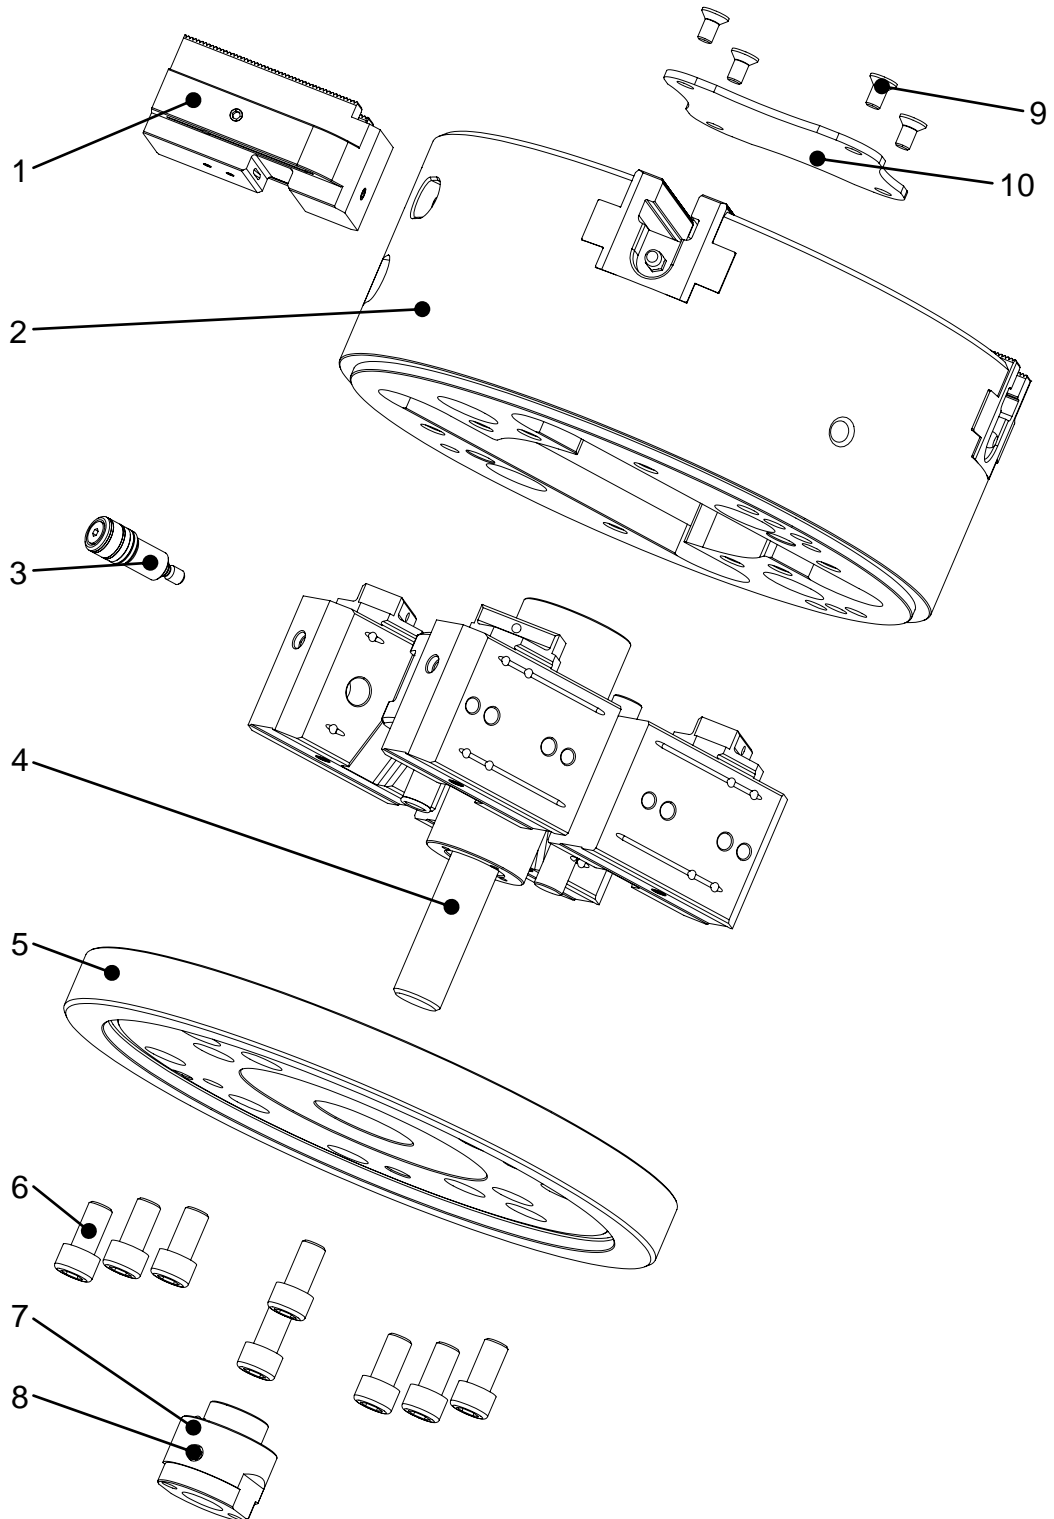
Démontage/montage du mandrin de serrage (VK021 - VK080)
